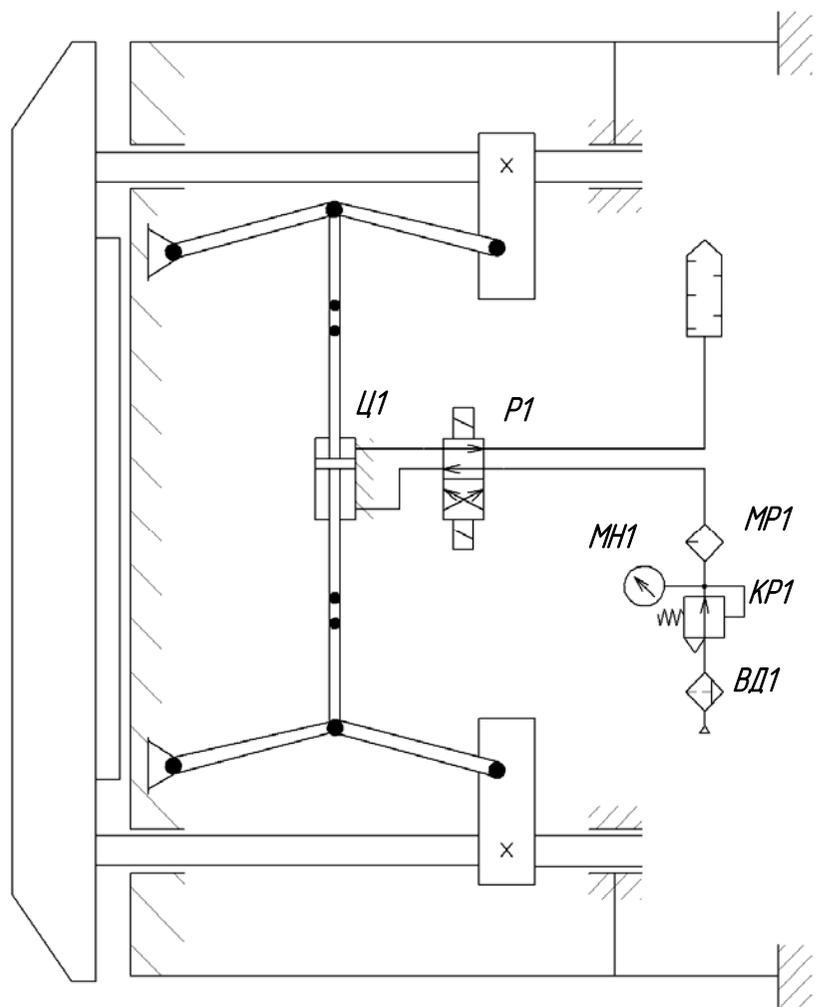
Пневматическая схема ножниц для рубки шпона НГ-18
